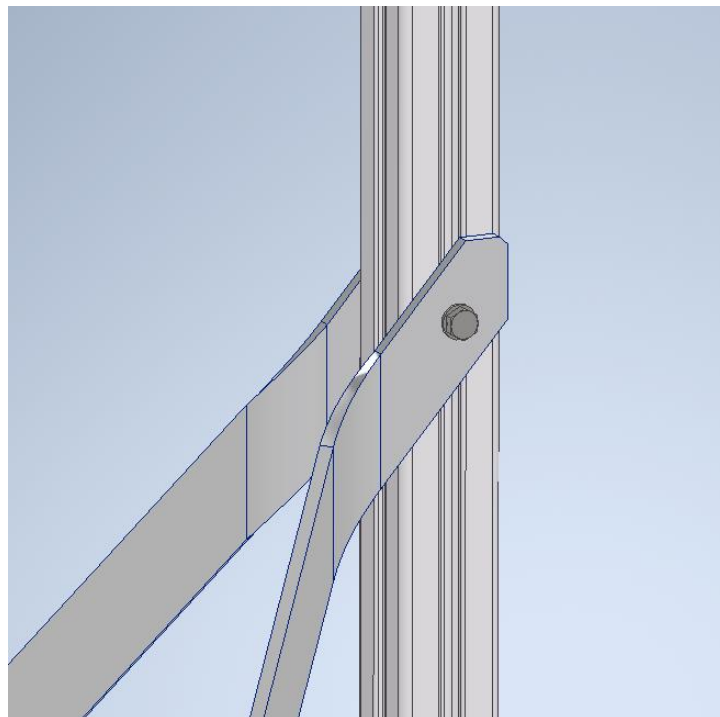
Detail připojení hlavního profilu ke spojovací desce
